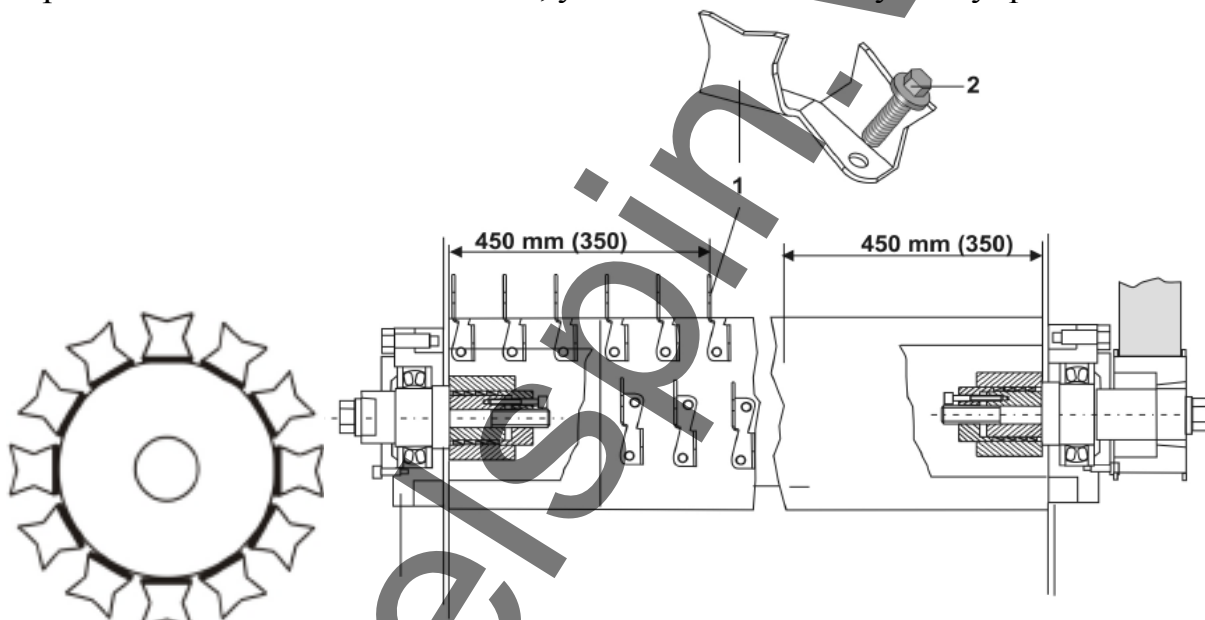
Конструкция ножевого барабана кипоразрыхлителей Unifloc A11
